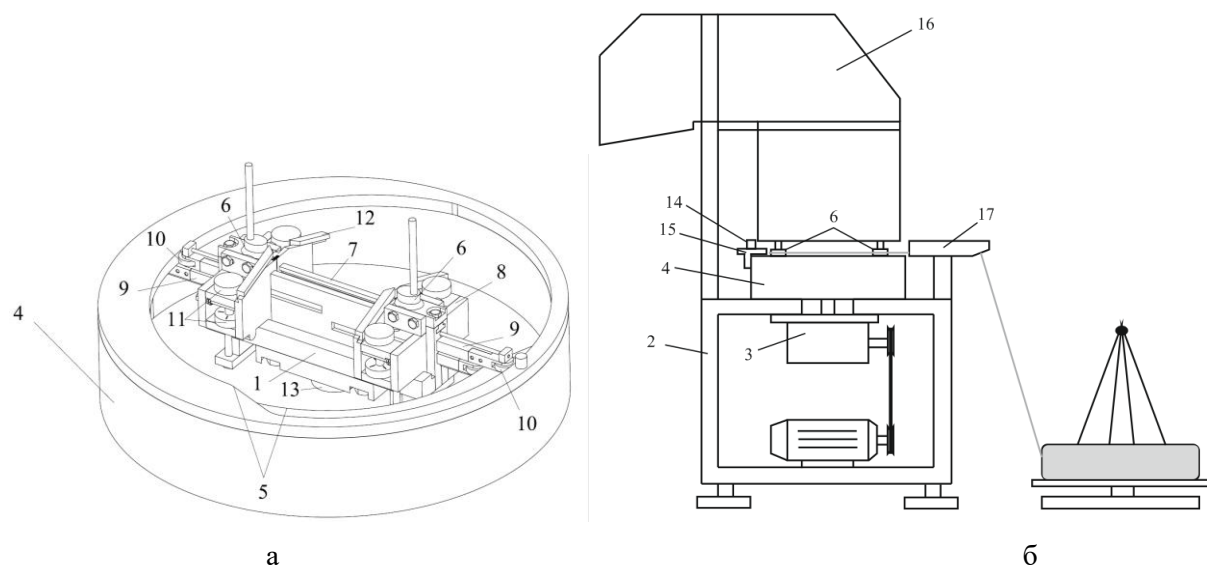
Станок для изготовления арматурного каркаса заданного профиля: а – навивочный цилиндр; б – общий вид станка
